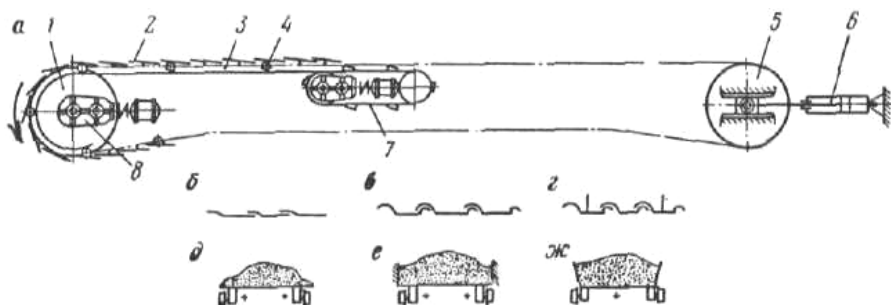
Принципова схема пластинчастого конвеєра і несучого полотна. На рисунку показані наступні види пластин: б – гладкі пластини; в – хвилясті пластини; г – пластини з поперечними перегородками; д – без бортів; е – з нерухомими бортами; ж – з рухливими бортами
